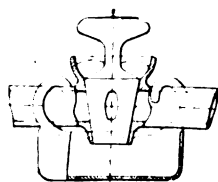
Vue schématique d'un robinet pour tube horizontal (M. A. Turpain).
